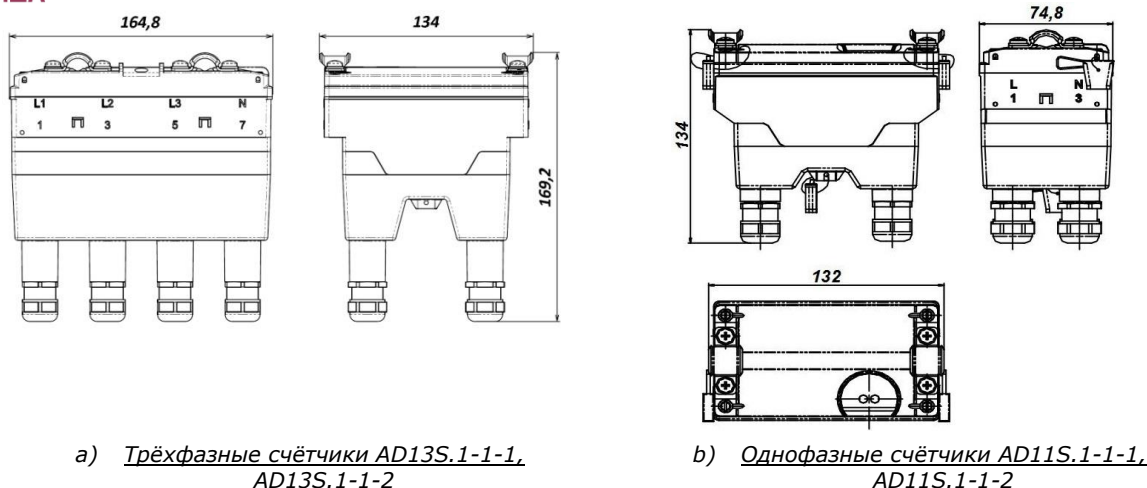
Габаритные размеры счётчиков в корпусе split
